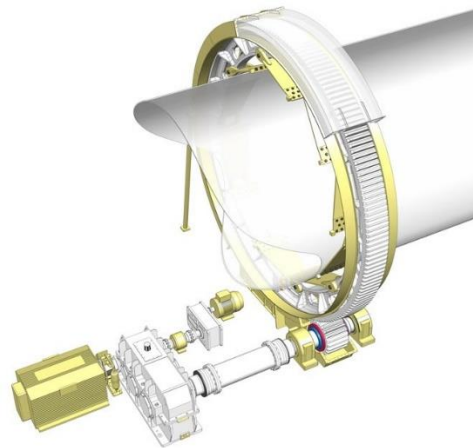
Загальний вигляд приводного механізму оберткової печі СМЦ-26
